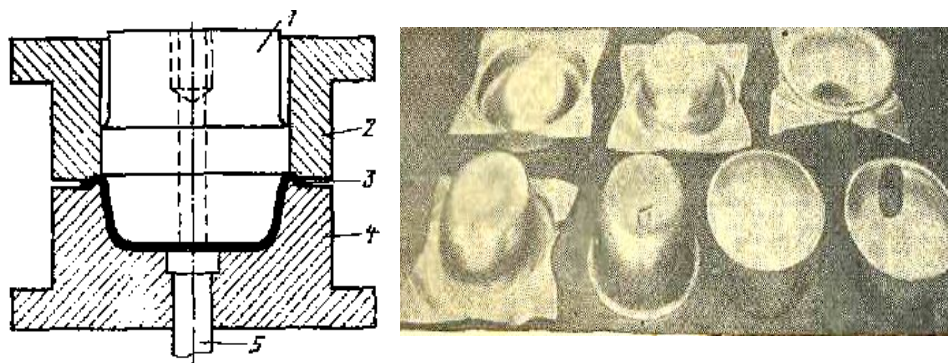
Схема витяжки й деталі, отримані за допомогою витяжки
